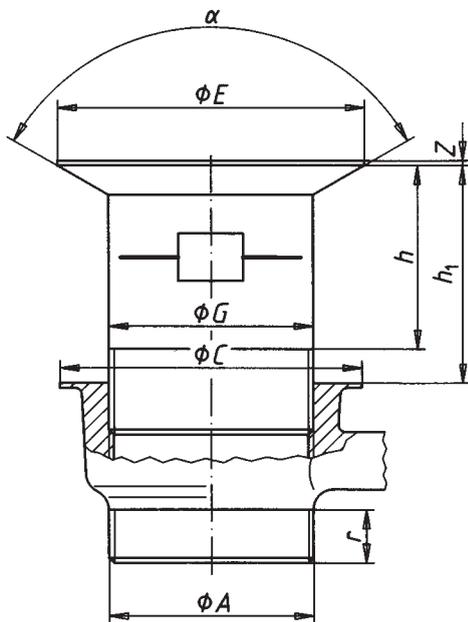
Schaftventil mit Überlauföffnung und mechanischer Betätigung
